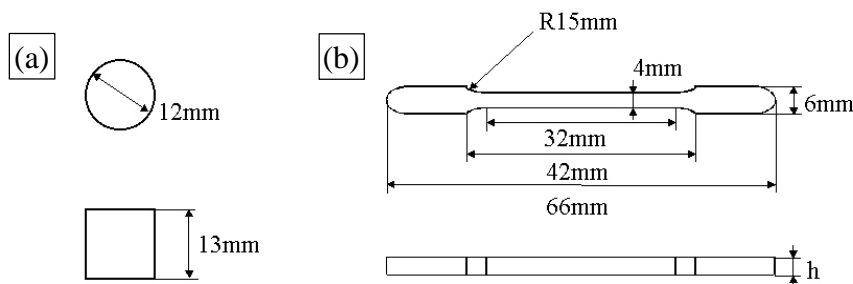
Geometría de las probetas a) cilíndricas y b) de tracción plana fabricadas.
